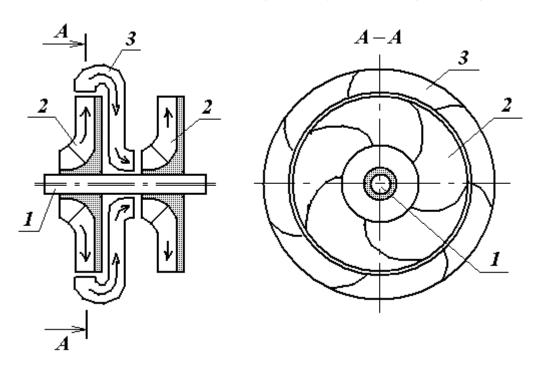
Схема установки направляющего аппарата: 1 - вал; 2 - ра-бочее колесо; 3 - направляющий аппарат
